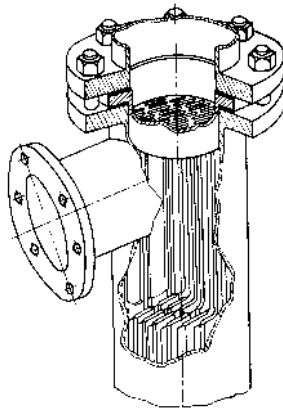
Вузол з'єднання плоскотрубного пучка з трубними решітками і корпусом
